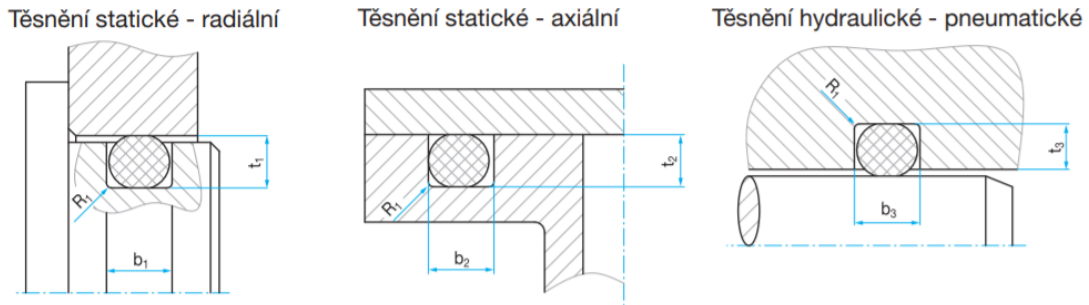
Princip těsnění pomocí o–kroužků [16]
